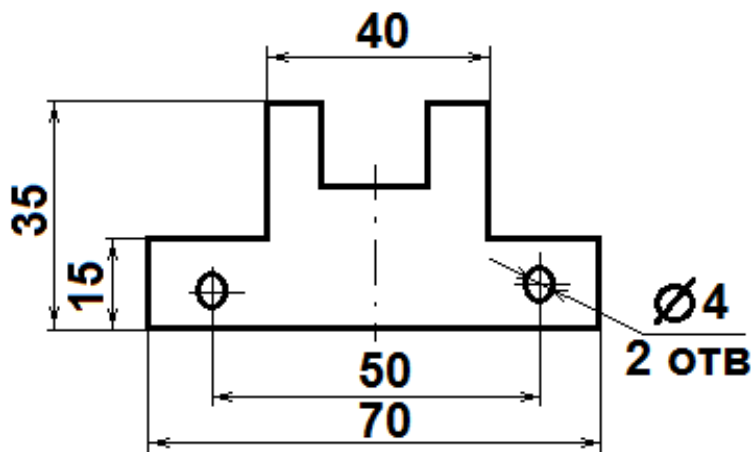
Чертеж с неполными данными изделия «Планка»
